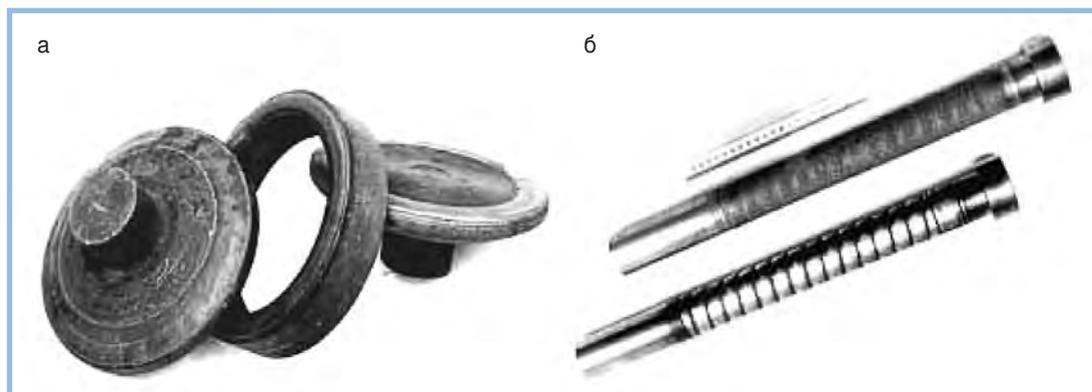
Внешний вид деталей задвижек для гидротранспортировки угля, наплавленных плазменно-порошковым способом: а — детали затвора; б — штоки
